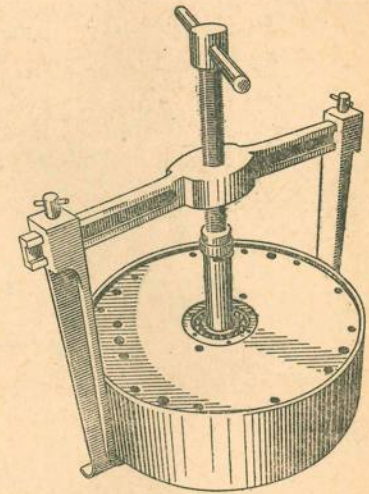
Выпрессовка ведущего валика бортового фрикциона при помощи приспособления
